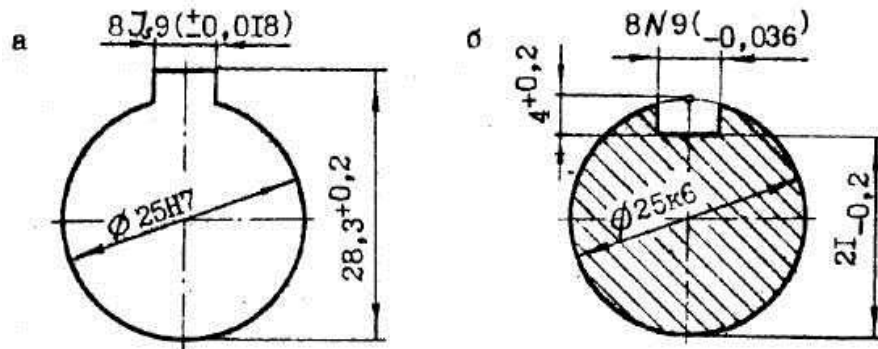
Позначення розмірів деталей шпонкового з'єднання: а-втулки, б-вала
